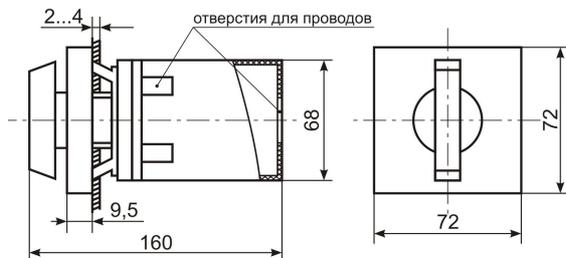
Габаритные размеры переключателя пакетного серии ПМО
